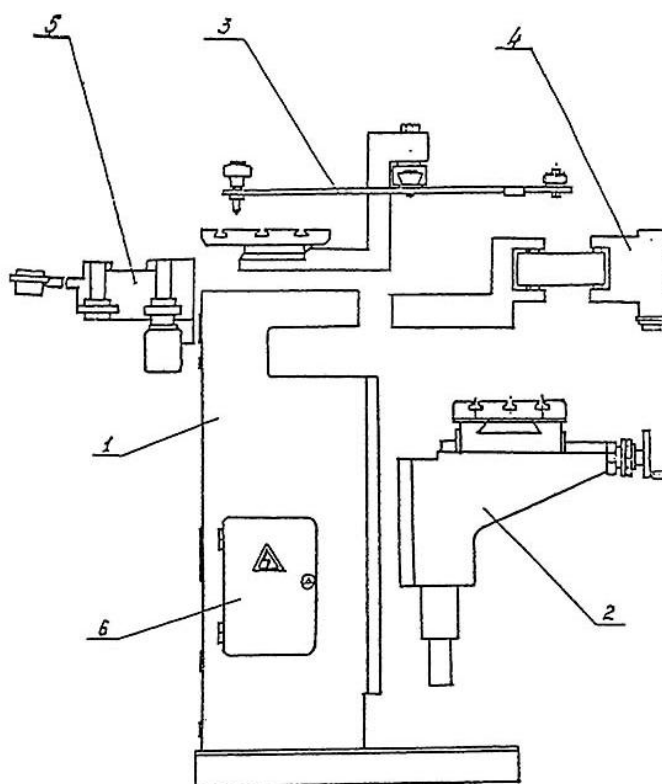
Розташування складових частин гравіювального верстата 6E463
